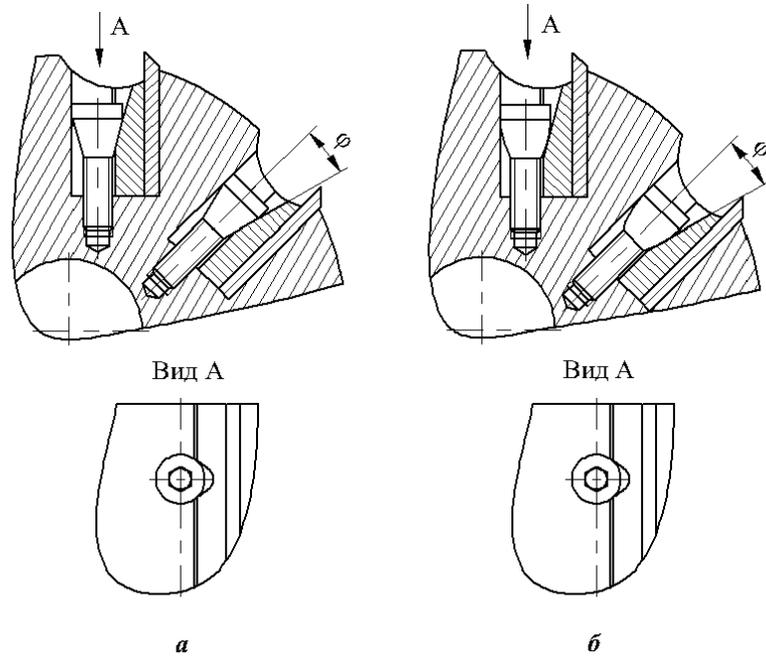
Узел крепления режущего ножа радиальным винтом: *а* – с коническо-цилиндрической головкой; *б* – с криволинейной в осевом сечении головкой
